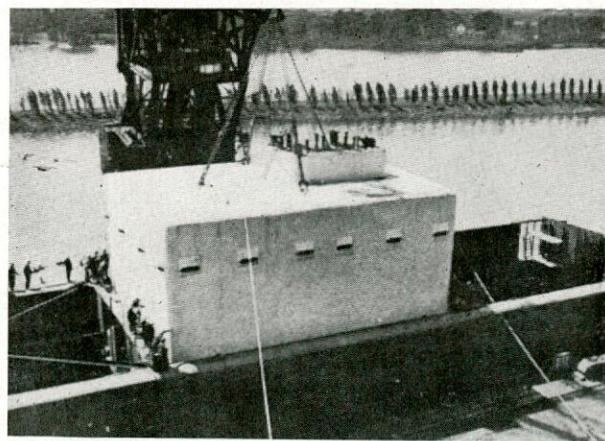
Colocación de un tanque a bordo, una vez aislado con espuma.
